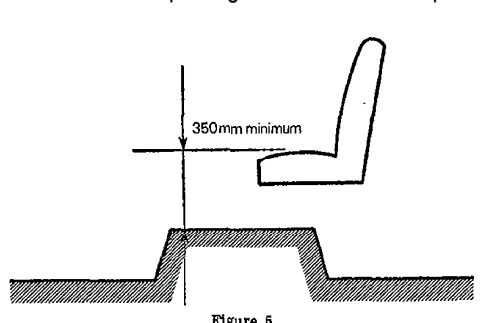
bis. Intrusion tolérée d'un passage de roue devant une place assise latérale
